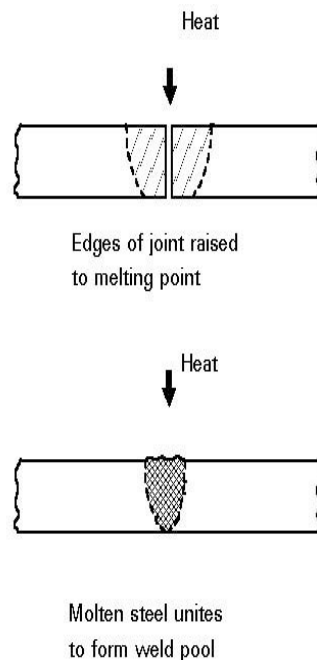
Formation d'une piscine de la soudure.
